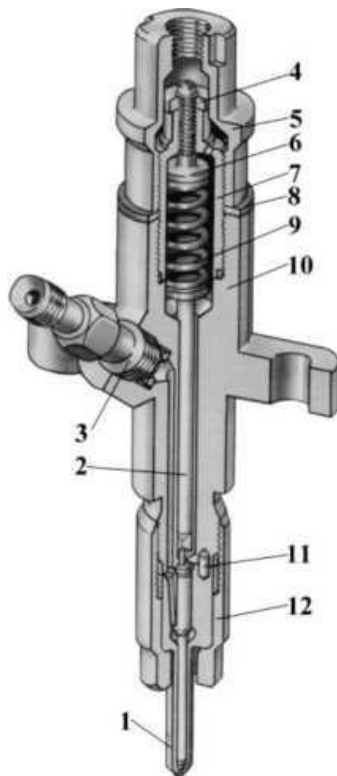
Устройство форсунки: 1 - распылитель; 2 - штанга; 3 - штуцер подвода топлива; 4- контргайка; 5 - колпак форсунки; 6 - регулировочный винт; 7 - гайка пружины; 8 - прокладка; 9 - пружина; 10 - корпус форсунки; 11 -штифты; 12 - гайка распылителя.
